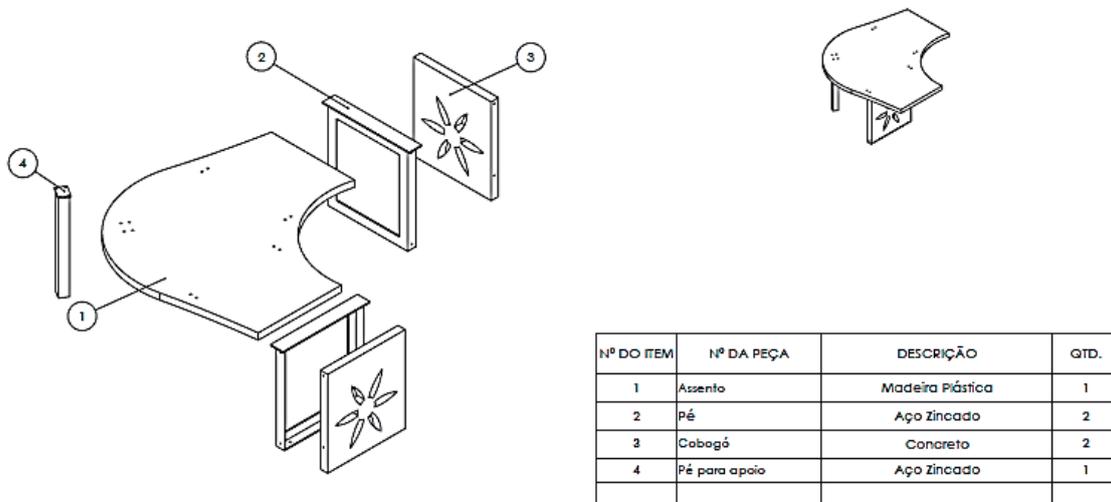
Desenho Técnico com Vista Explodida do Banco, São Sepé, 2016.
